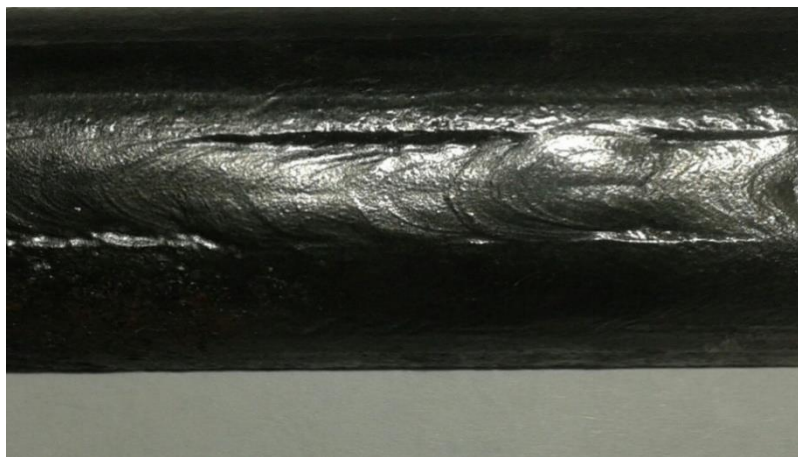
Образец сварки трубы из стали, вид наружного шва сверху
